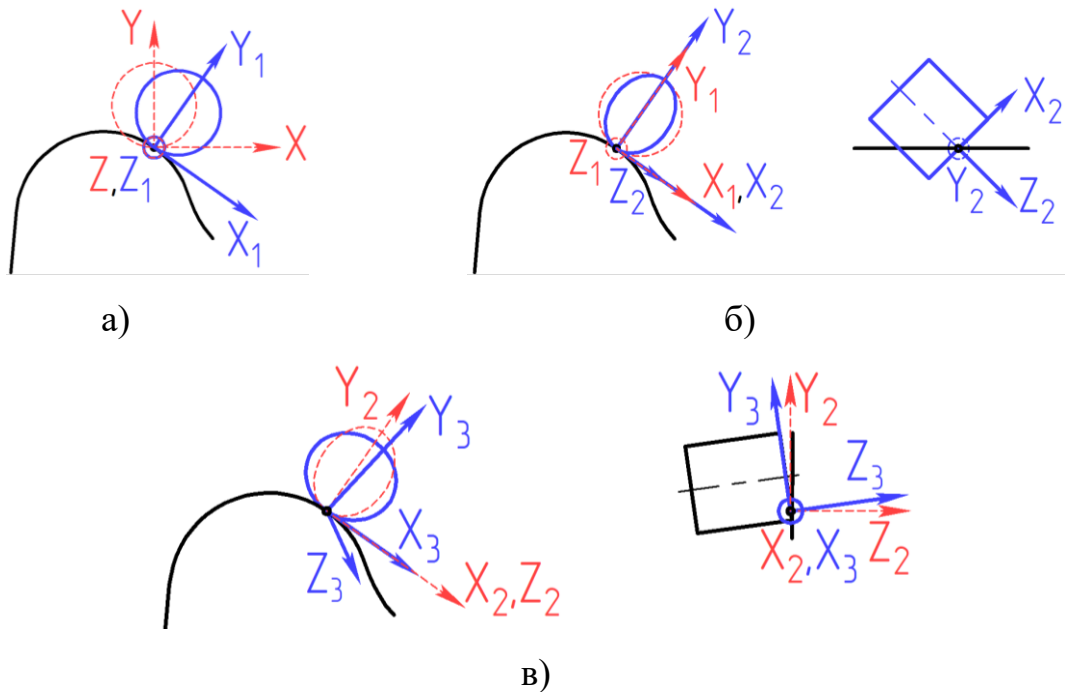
Схема определения положения СМП в корпусе сборной фасонной фрезы.
